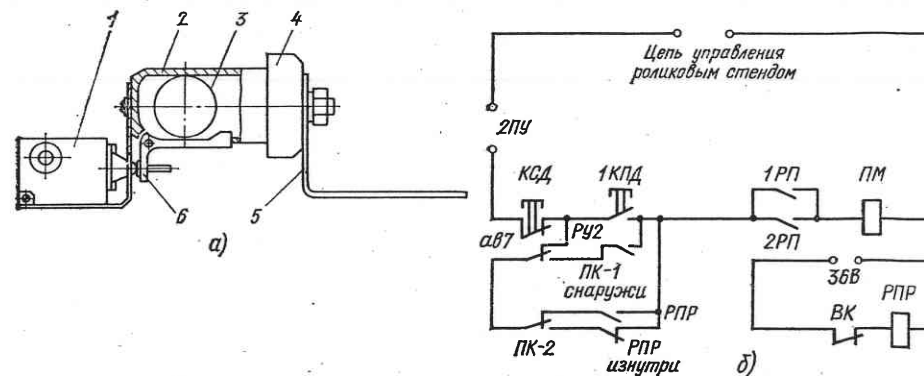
Гравитационный регулятор положения сварочного автомата на обечайке при сварке кольцевых поворотных стыков:
